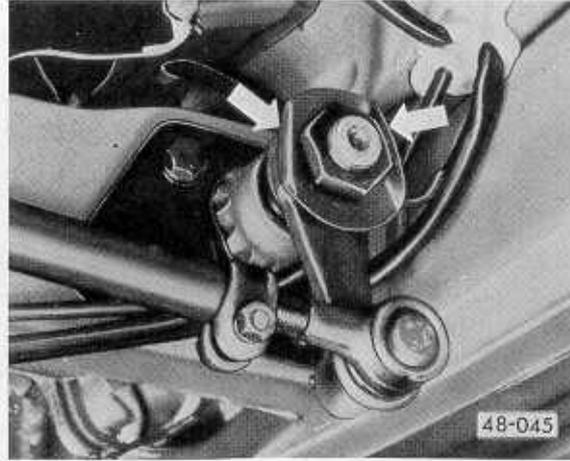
Befestigungsmutter für Lenkstockhebel sichern.
